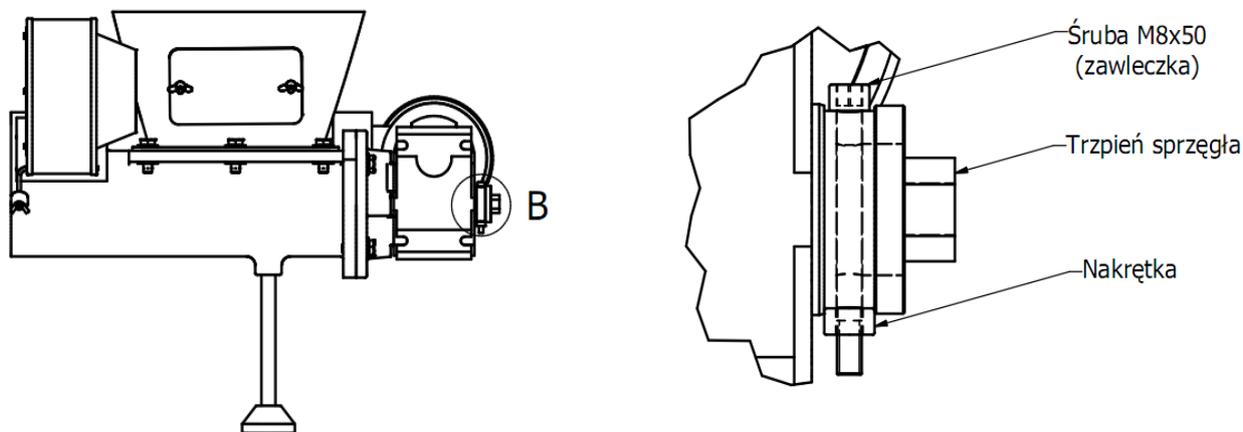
Способ установки задвижки моторредуктора со шнеком
